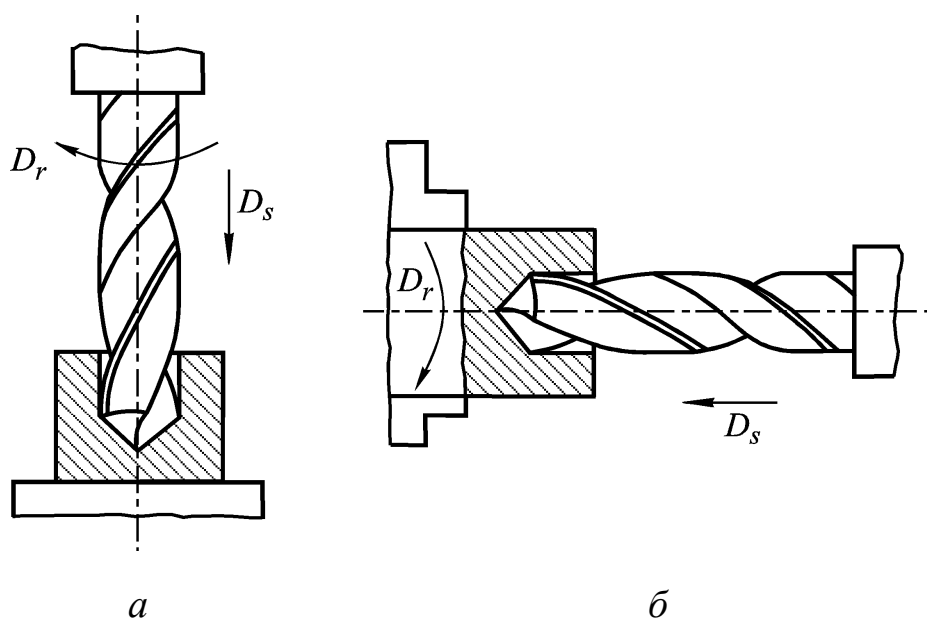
Схемы обработки отверстий на сверлильных (*а*) и токарных (*б*) станках
